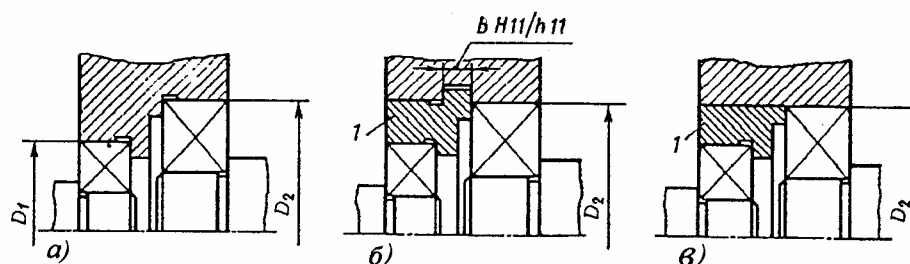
Конструктивные варианты выполнения промежуточной опоры во внутренней стойке корпуса при установке подшипников "враспор":
